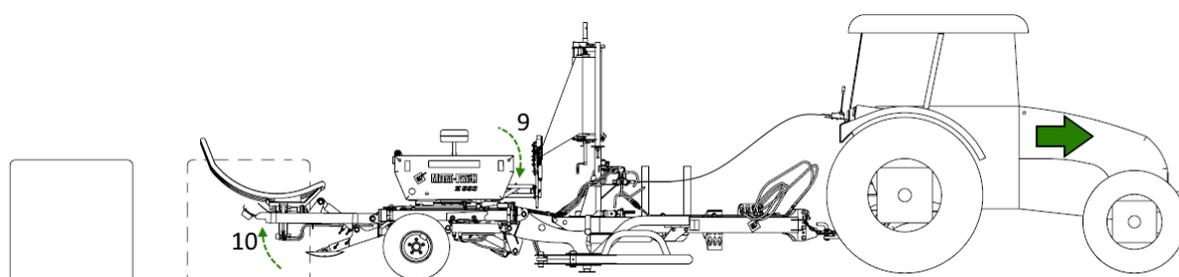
Levage du plateau de travail et du dispositif de positionnement des balles
